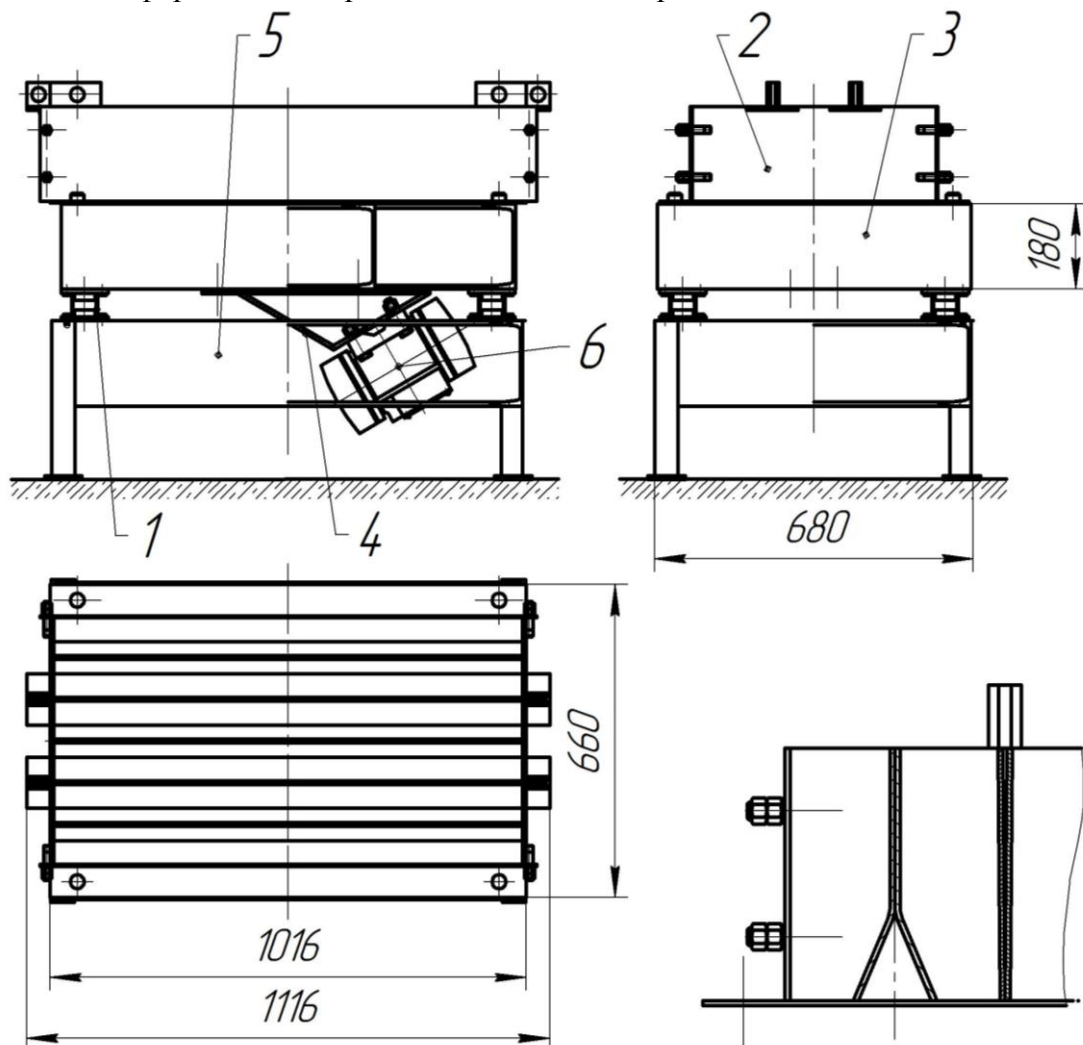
Установка для виготовлення бордюрного каменю та тротуарної плитки.
